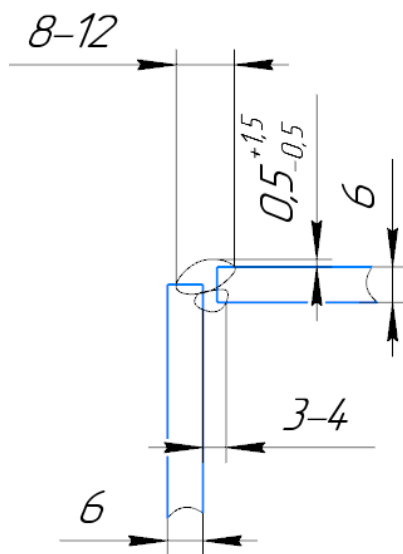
Разделка кромок и размеры сварного шва У5 ГОСТ 5264-80
